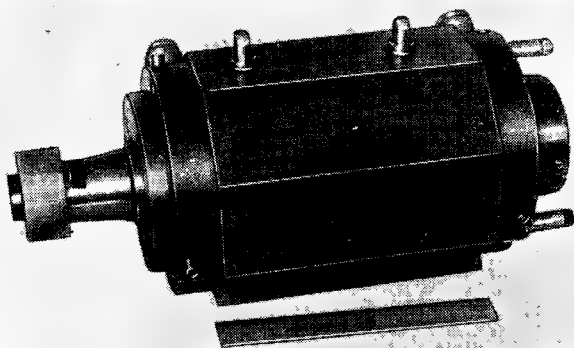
а. Общий вид электрошпинделя ЭШ-12/5.0 новой конструкции с водяным охлаждением в корпусе.
